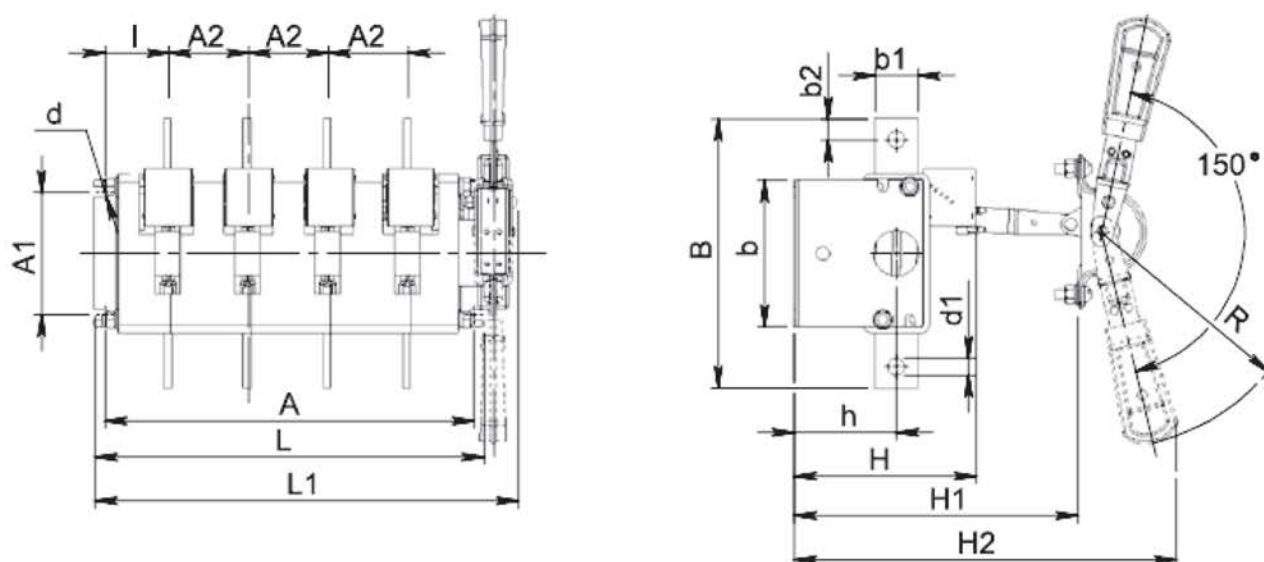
Выключатель-разъединитель четырехполюсный на два направление с боковой рукояткой.
